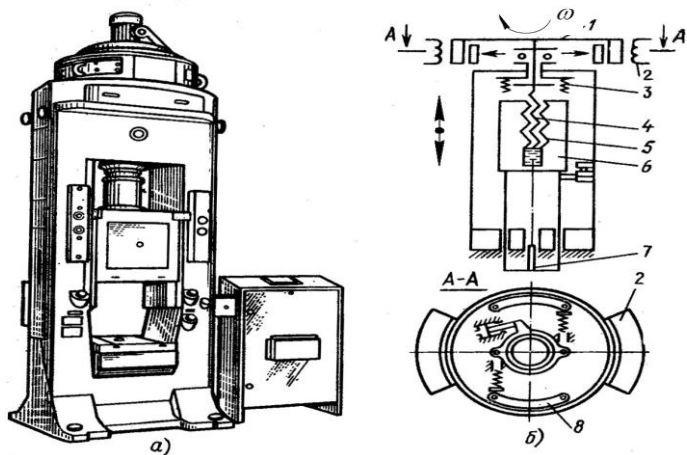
Схема гвинтового преса із дугостаторним приводом: а – загальний вигляд; б – кінематична схема; 1 – ротор-маховик; 2 – дугові статори; 3 – амортизатори; 4 – гвинт; 5 – гайка; 6 – повзун, 7 – виштовхувач; 8 – гальмо
